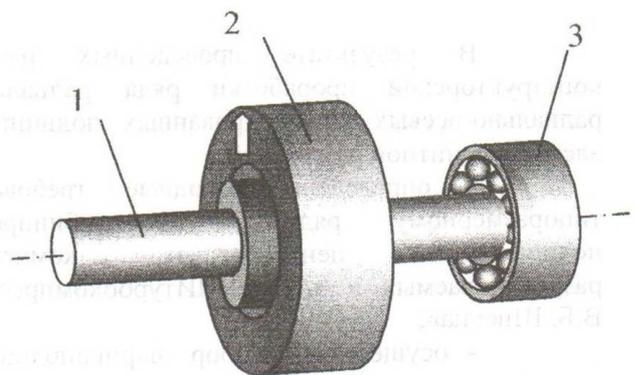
Конструктивная схема комбинированного подшипника: 1- ротор; 2- устройство электромагнитной разгрузки; 3- шарикоподшипник
